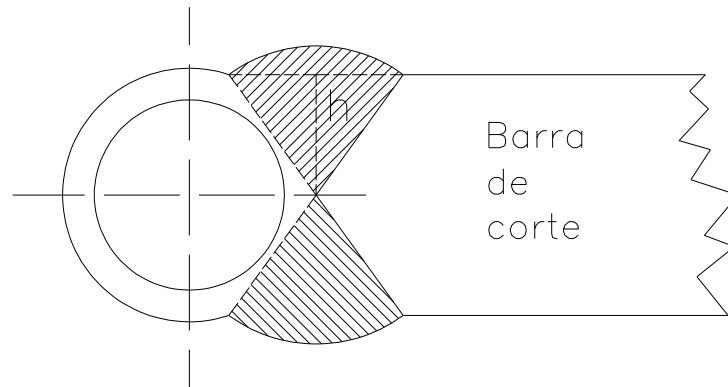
De la barra de corte con el buje soldado vista lateral
